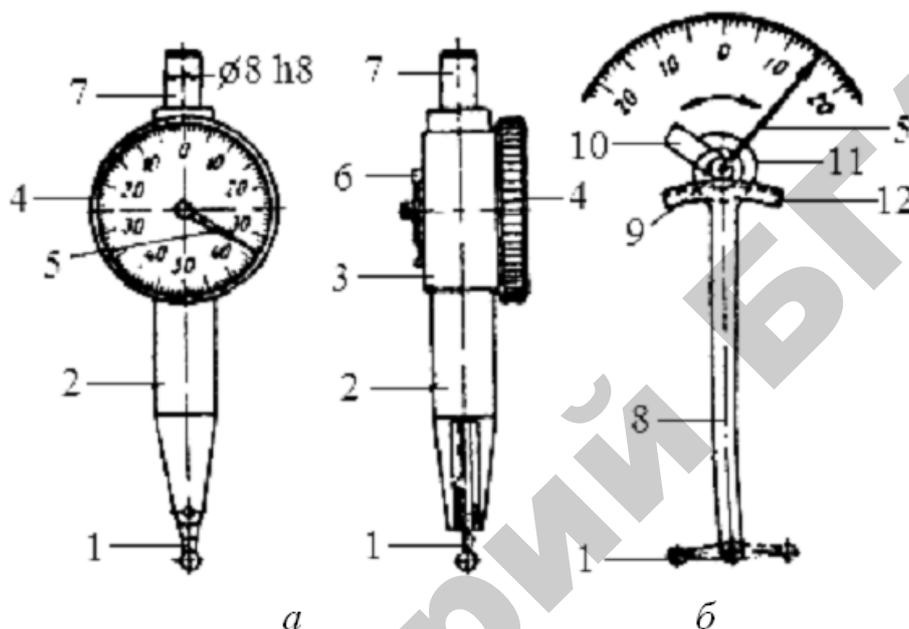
Рычажно-зубчатый индикатор (а) и его схема (б):
